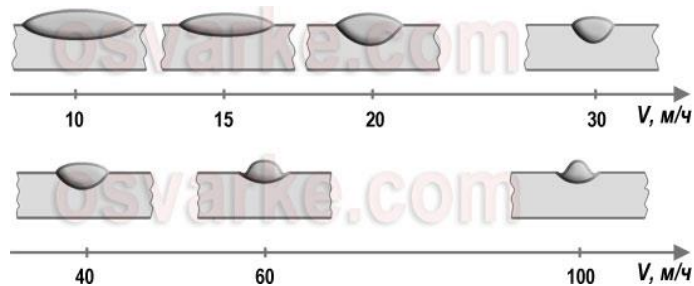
Влияние скорости сварки на форму и размеры шва
